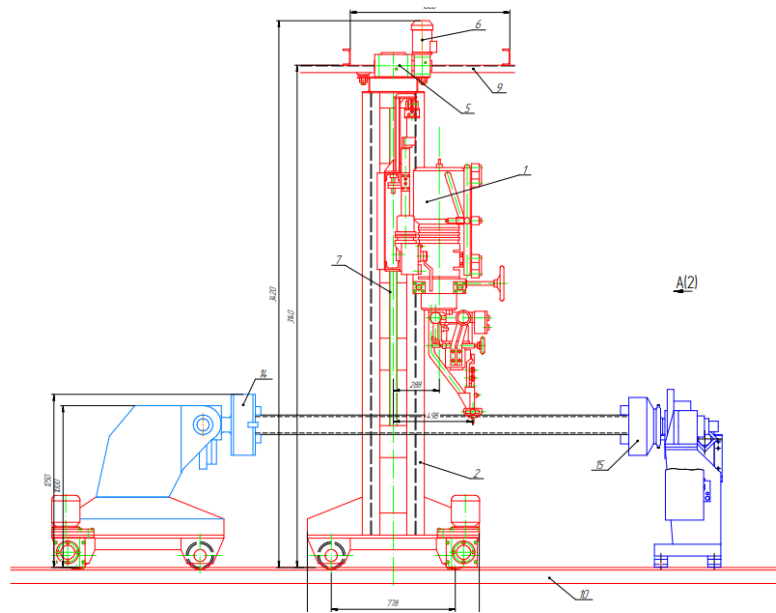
Схема компонування обладнання для зварювання прямолінійних швів
